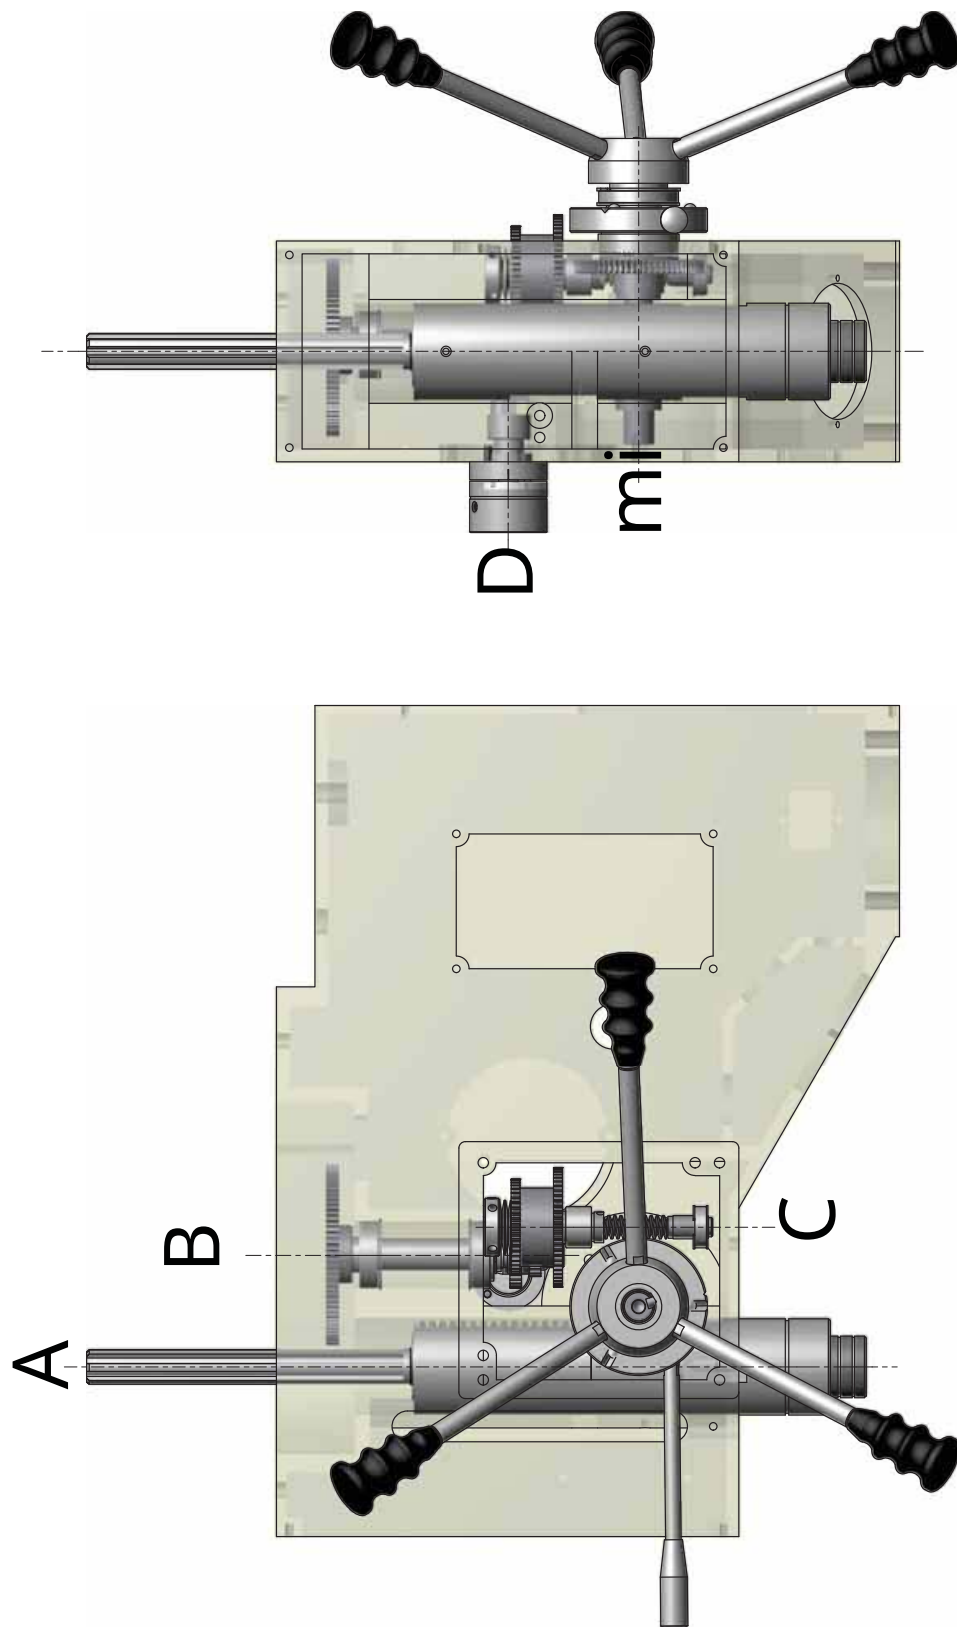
Vorschubgetriebe - Caja de engranajes de alimentación
